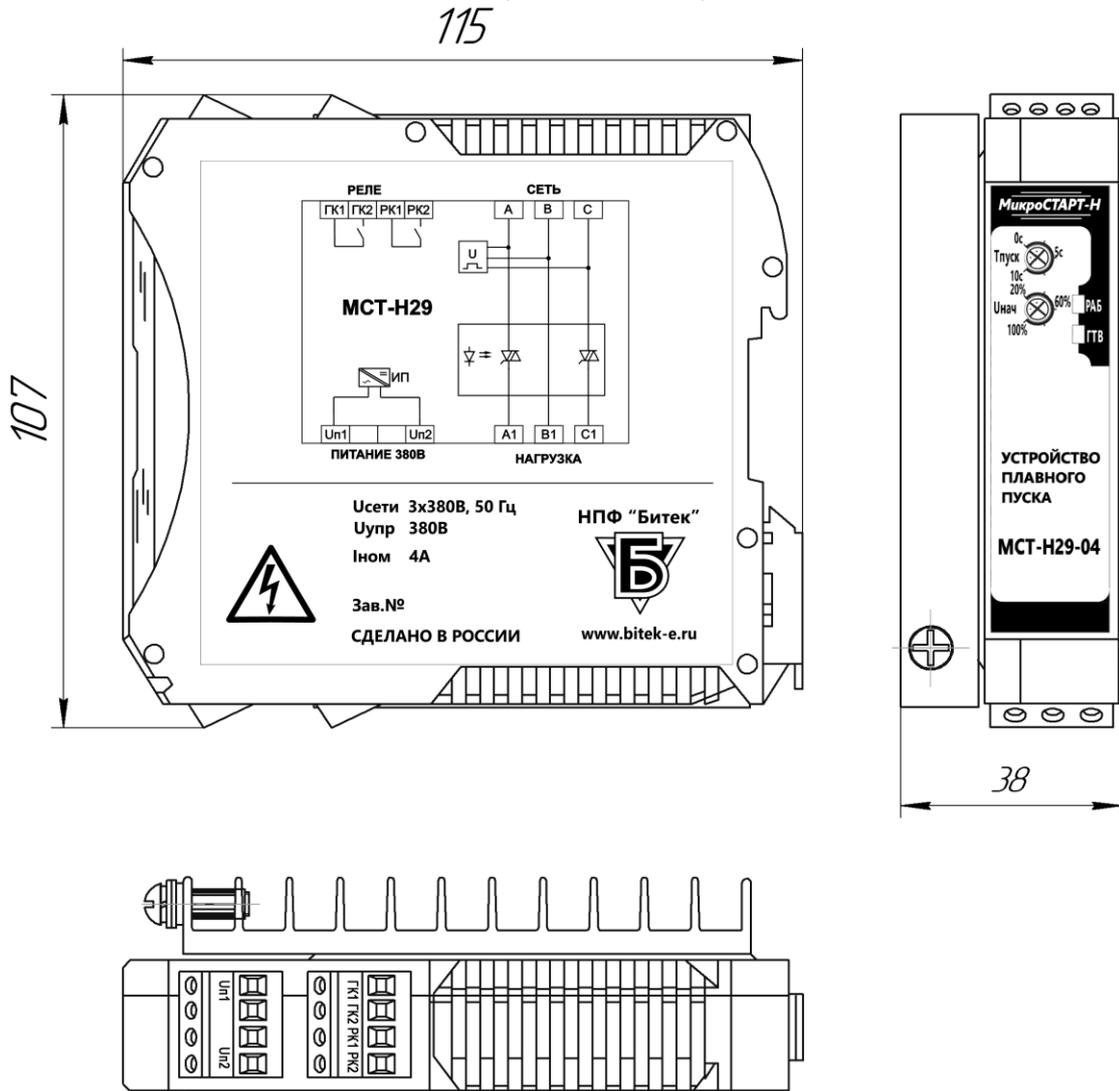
Габаритно-установочные размеры МСТ-Н29-04
